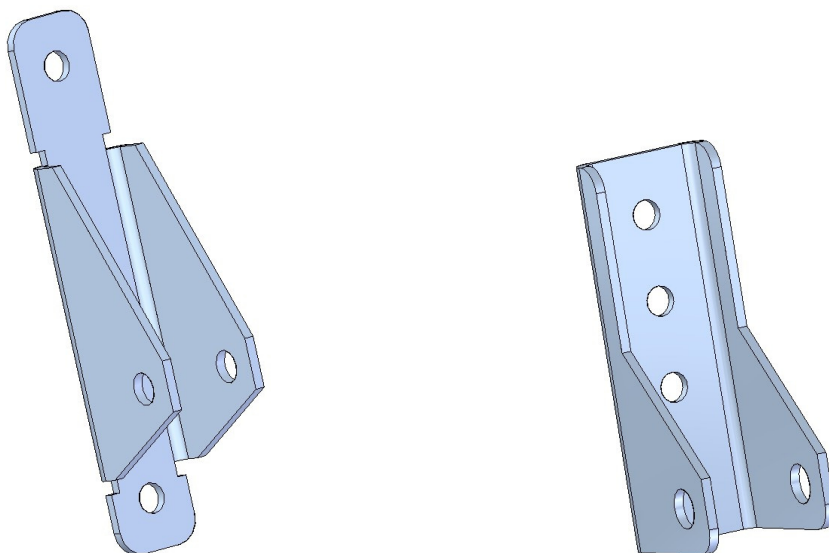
Ramkonsoler: a) KR-1-23 (till MCR-Sx motorer), b) KR-2-25 (till MCR-Wx motorer)
